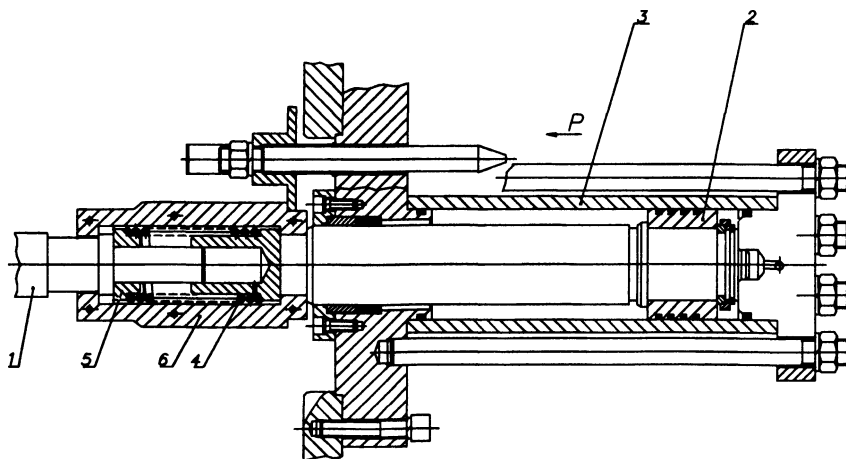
Элемент прессующего механизма машины литья под давлением для удаления пресс-остатка
